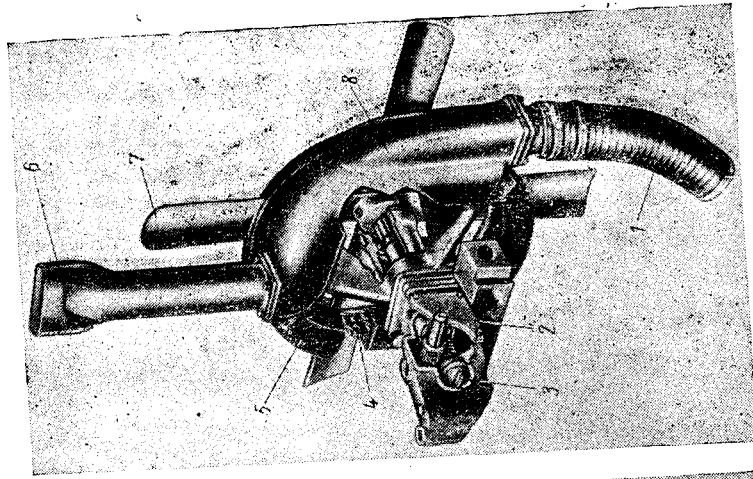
Буферный цилиндр дизель-компрессора Р42:
